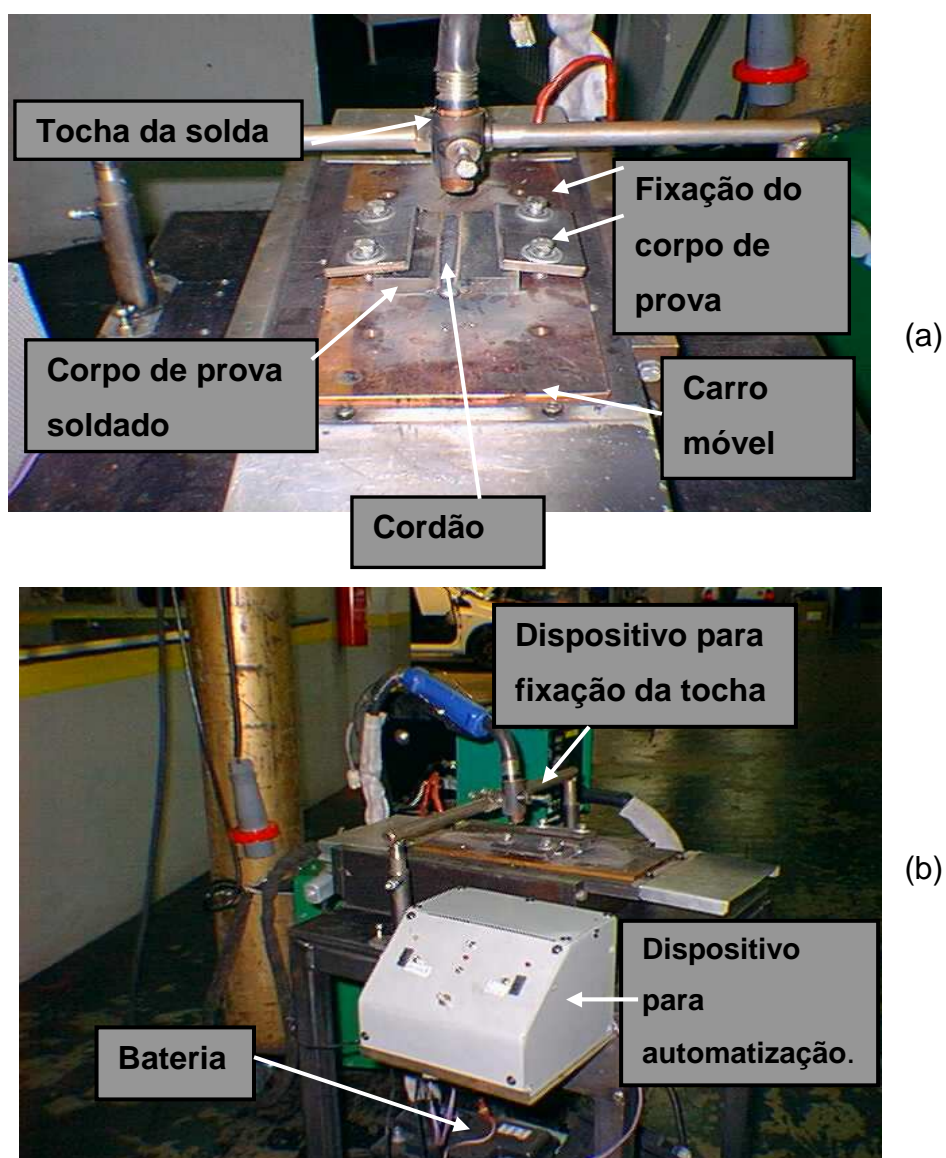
Dispositivo desenvolvido e utilizado na máquina de solda GMAW mostrando a fixação da tocha (a) e o conjunto montado responsável pela automatização do processo de soldagem (b).
